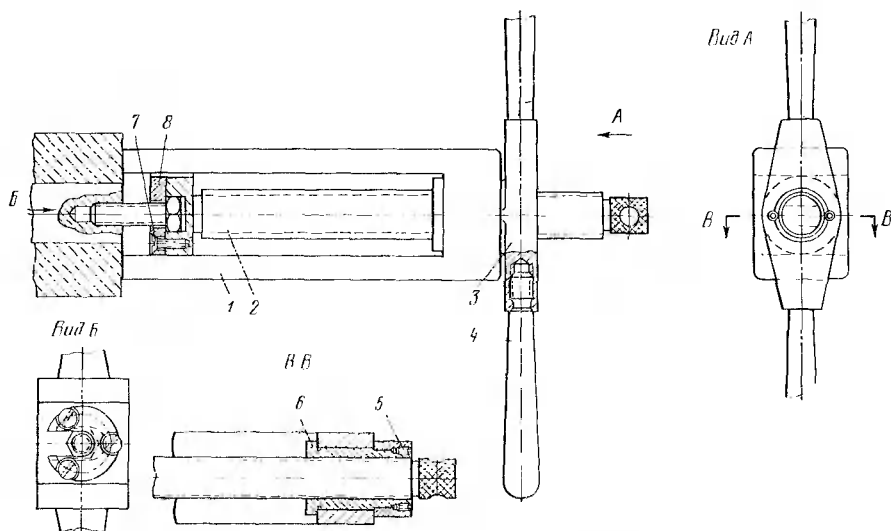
Приспособление для выпрессовки оси блока шестерен заднего хода:
